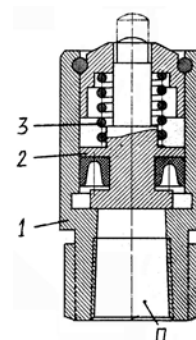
Штоковый индикатор давления: 1 – корпус; 2 – поршень со штоком; 3 – пружина; П – входной канал
